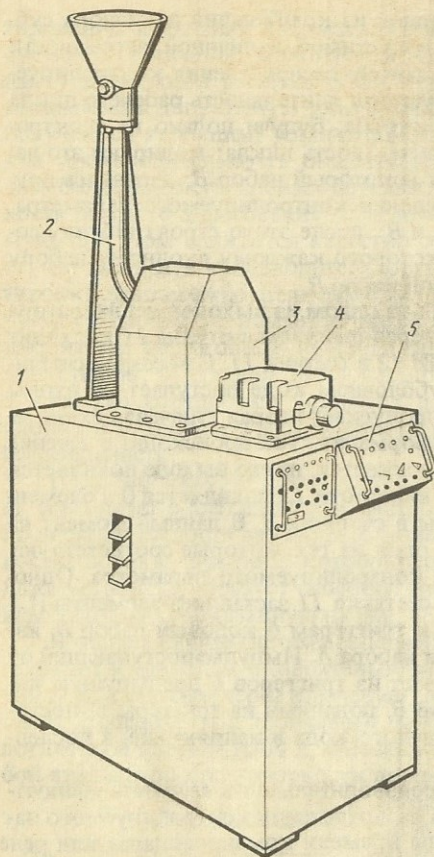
Автомат для сортировки заготовок поршневых пальцев
